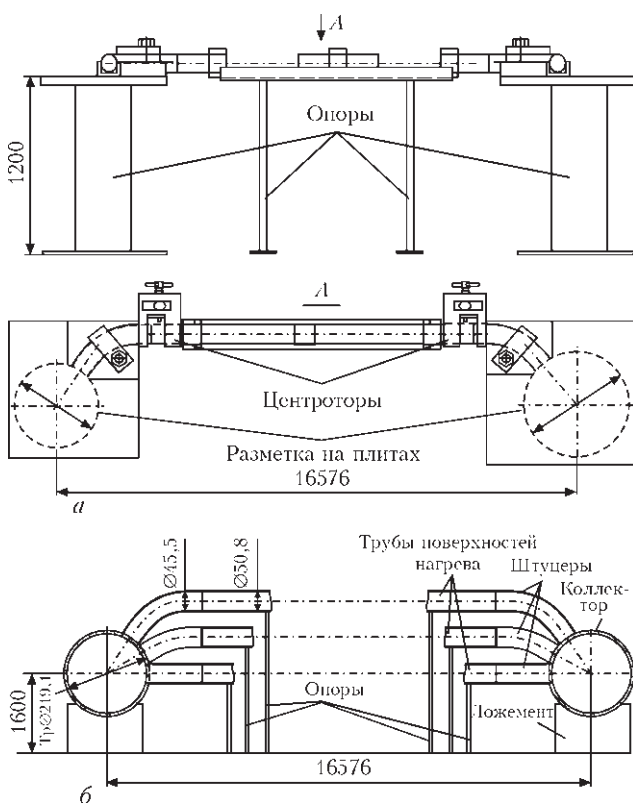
Стенды для сборки и сварки: а — стыковых соединений труб поверхности нагрева со штуцерами; б — угловых соединений коллектора с «трубной плетью»
